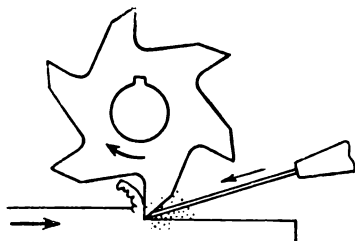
Схема охлаждения зуба фрезы тонкой струей
